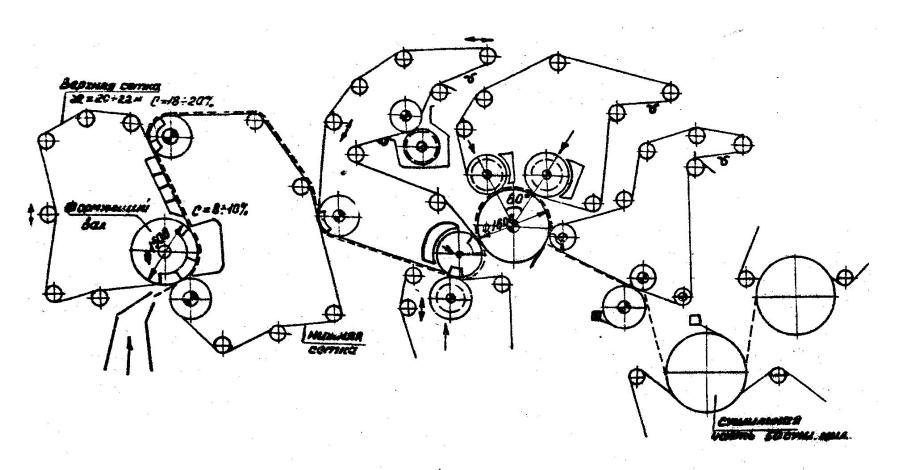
Схема бумагоделательной машини с формующим устройством "Дуоформер": (фирма Фойт) и прессовой частью "Сим-пресс" (фирма Валмет).
